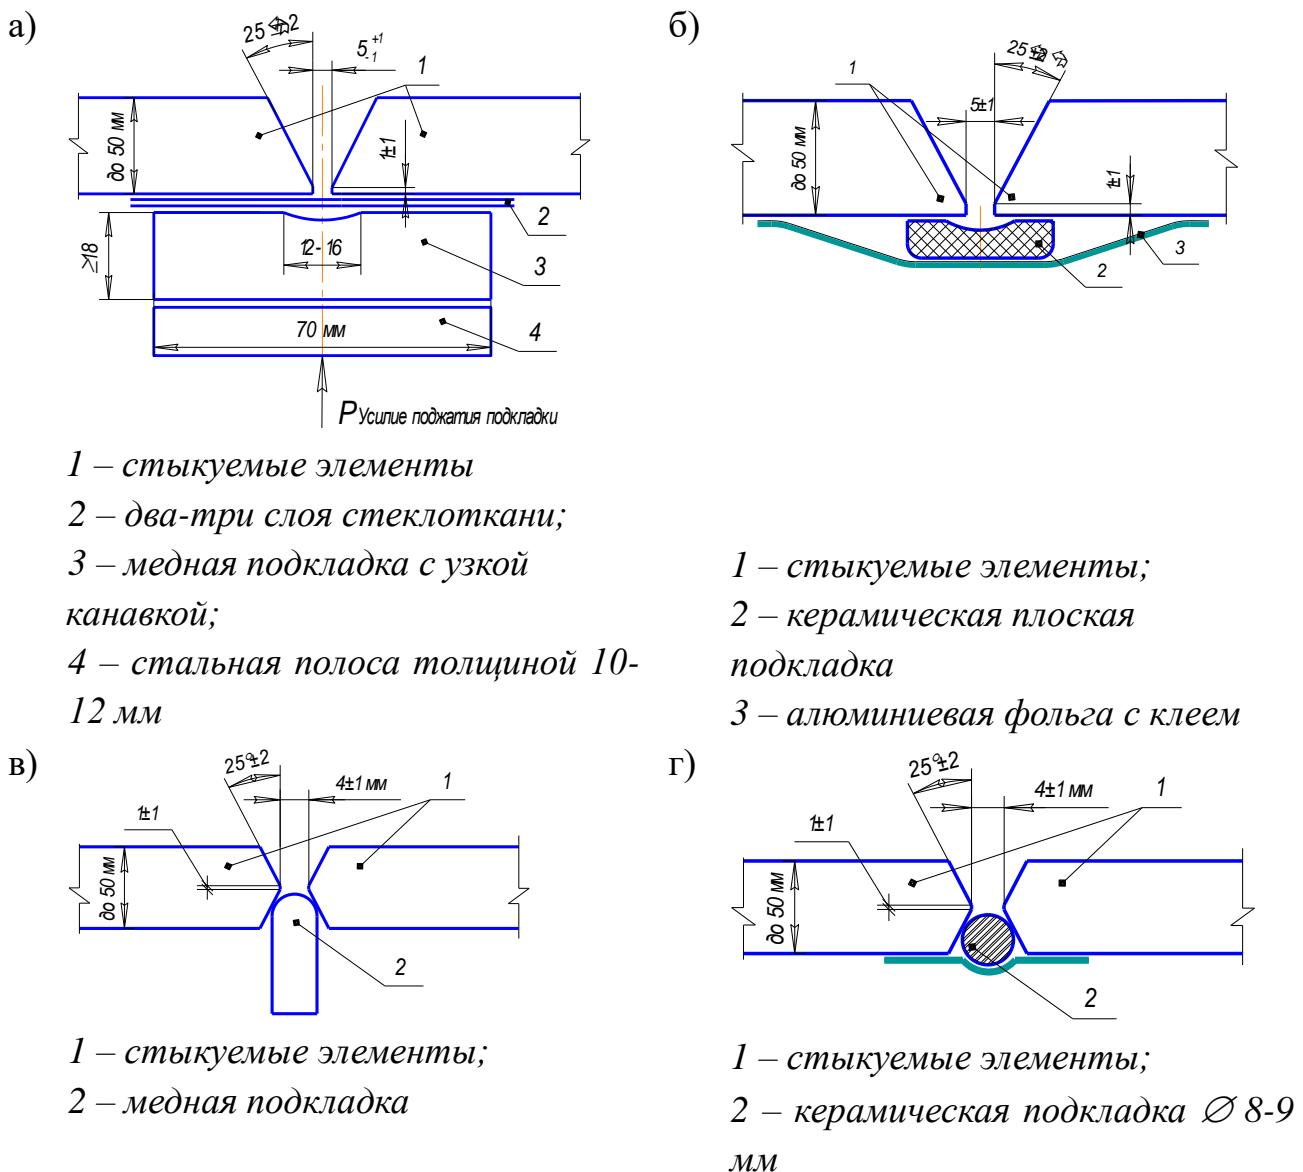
Схемы сборки монтажных стыковых соединений под ручную дуговую сварку покрытыми электродами
